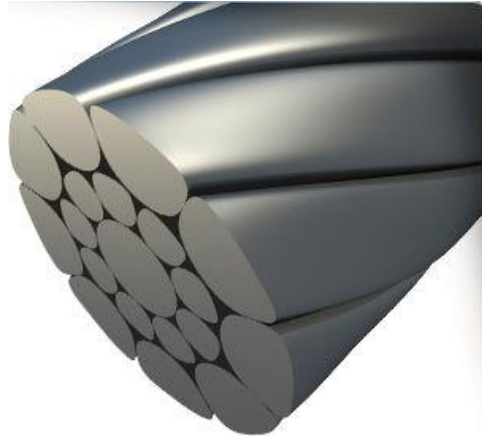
Perfil y sección de Dyform. Fuente: *Bridon International Ltd.
